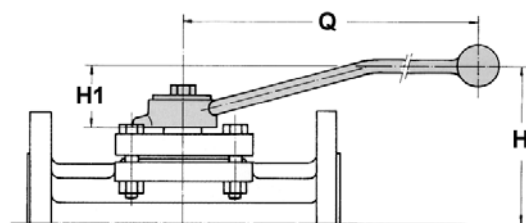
Рукоятка с шаровой головкой для кранов небольших размеров
